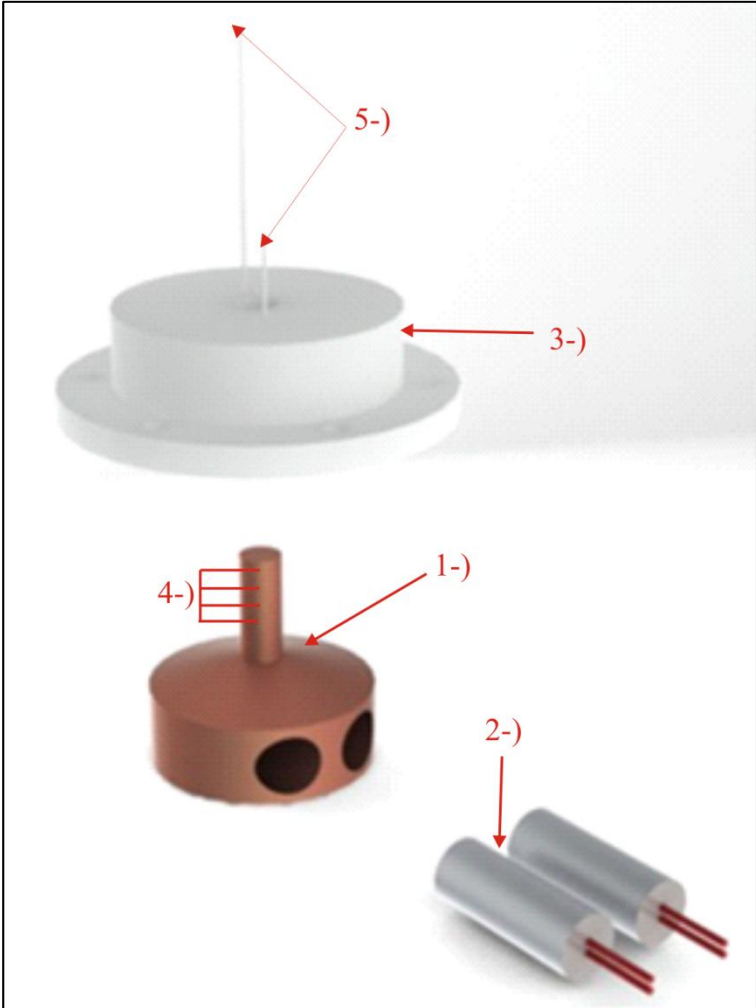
Seção de teste - Vista Explodida (SolidWorks)
